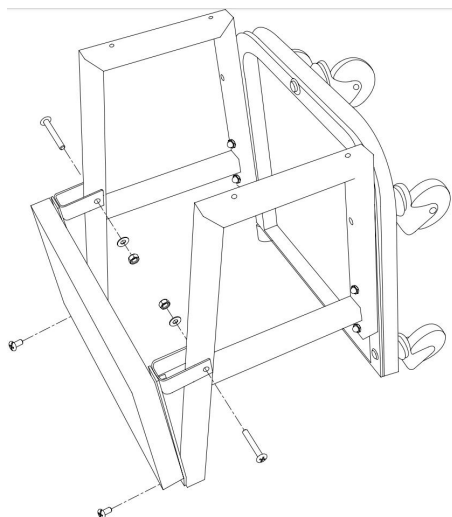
Zusammenbau von Werkzeugablage und Rollen
